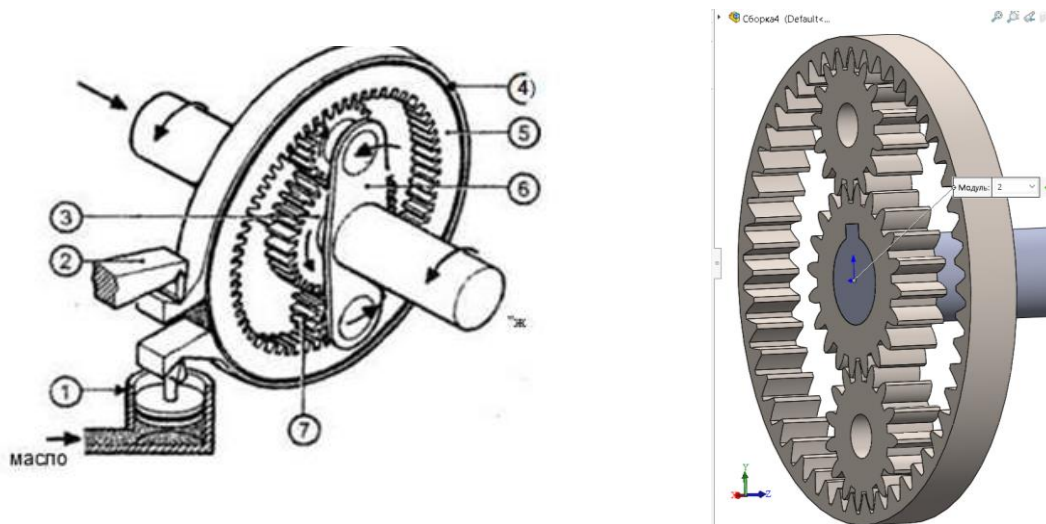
Простая планетарная передача: 1 – тормоз; 2 – неподвижный якорь; 3 – солнечная шестерня; 4 – тормозная накладдка; 5 – кольцевая шестерня; 6 – пластина водила; 7 – сателлит
